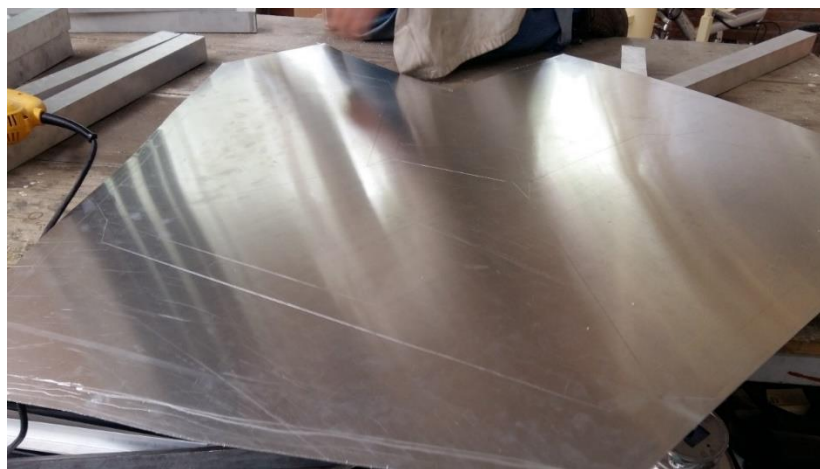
Croquis de la Fig. 144 dibujado en lámina de aluminio y cortado con caladora
